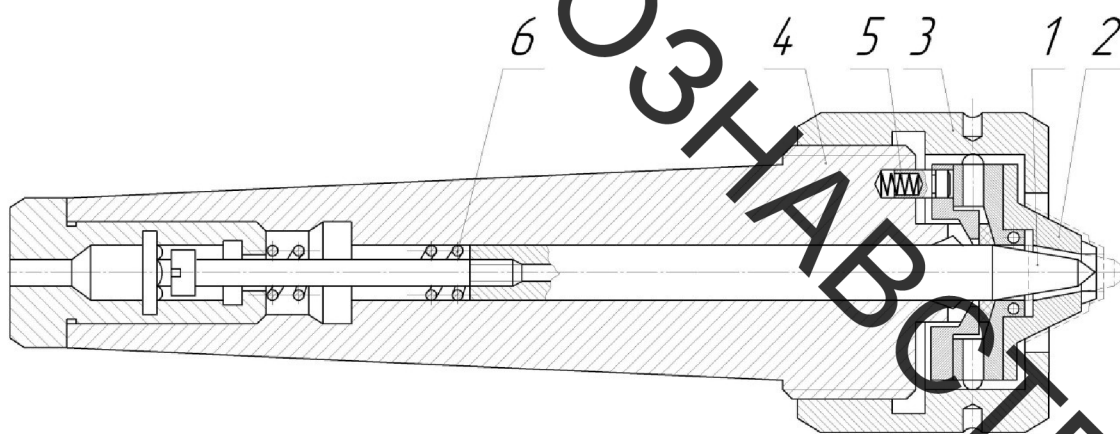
Повідковий центр (в установочному положенні)
